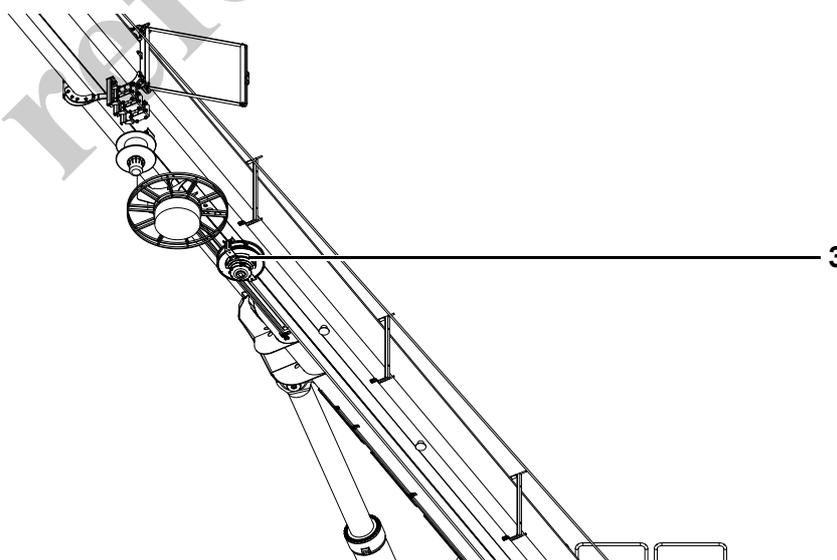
Transmisor de largo y ángulo/tambor de cable de resorte (3)
